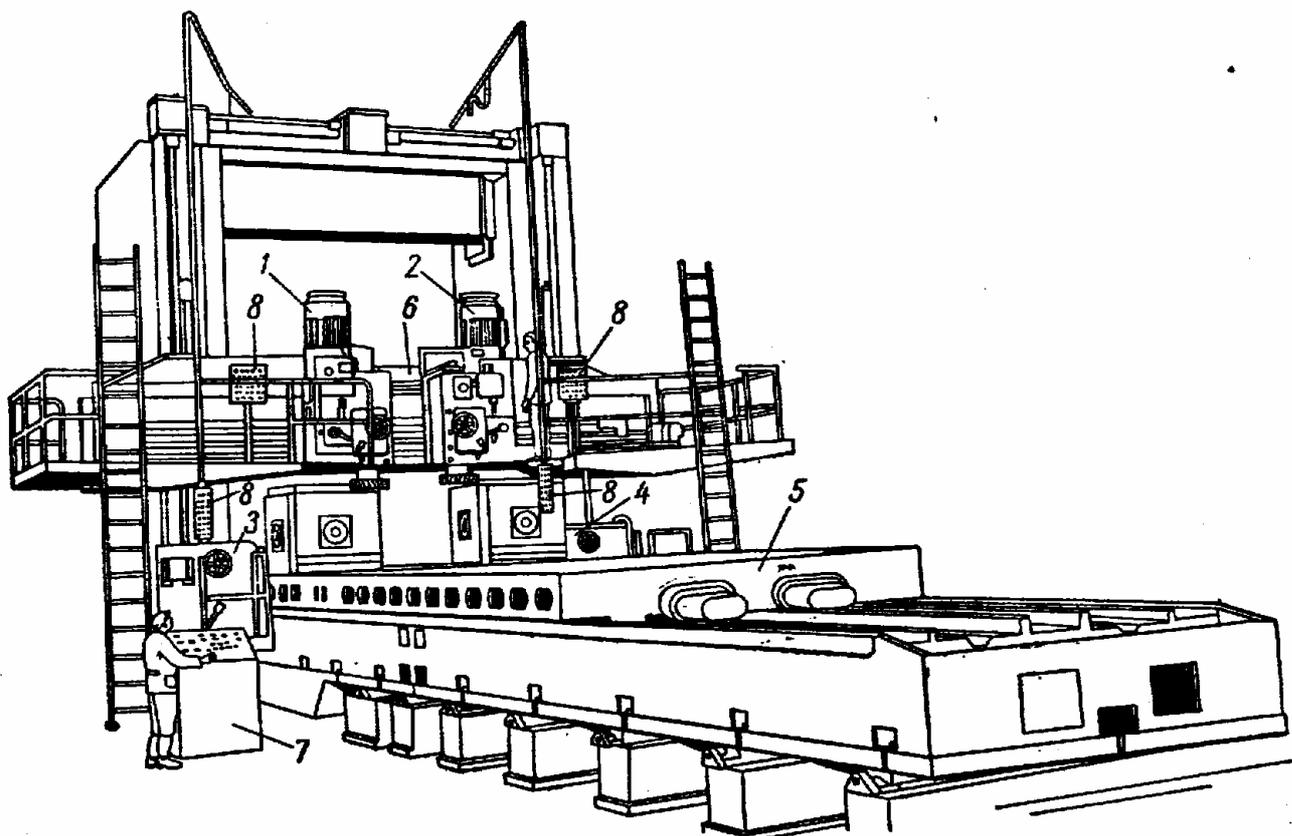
Многошпиндельный двухстоечный продольно- фрезерный станок 6682<sup>4</sup>
